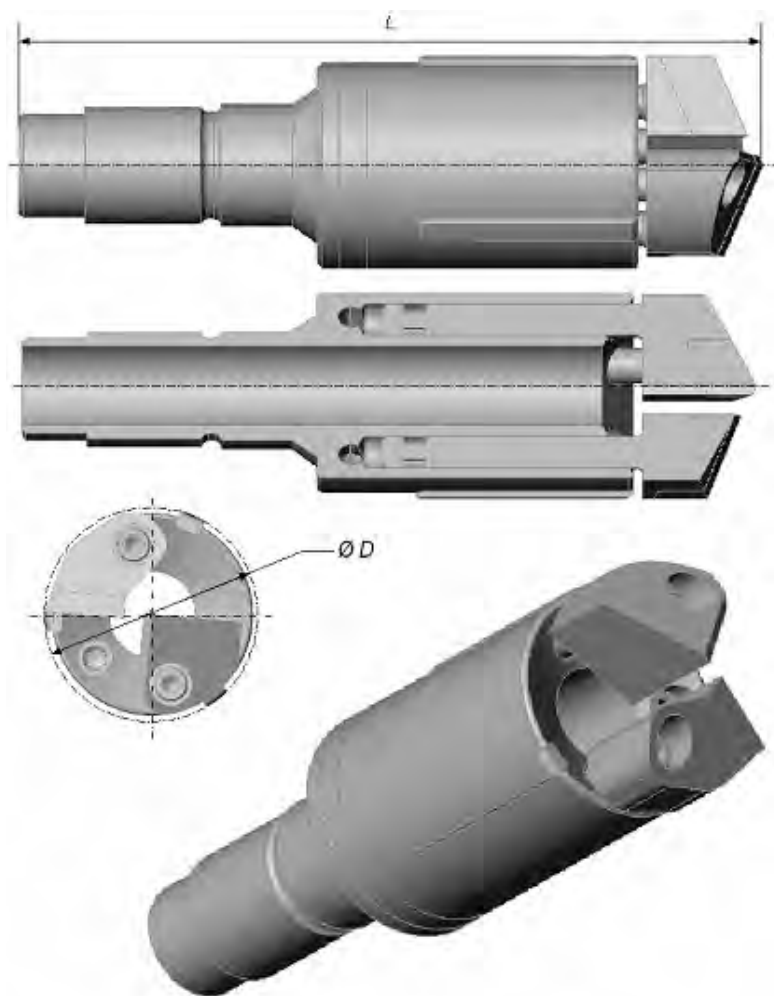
Конструкція адаптивного свердла ежекторного типу
